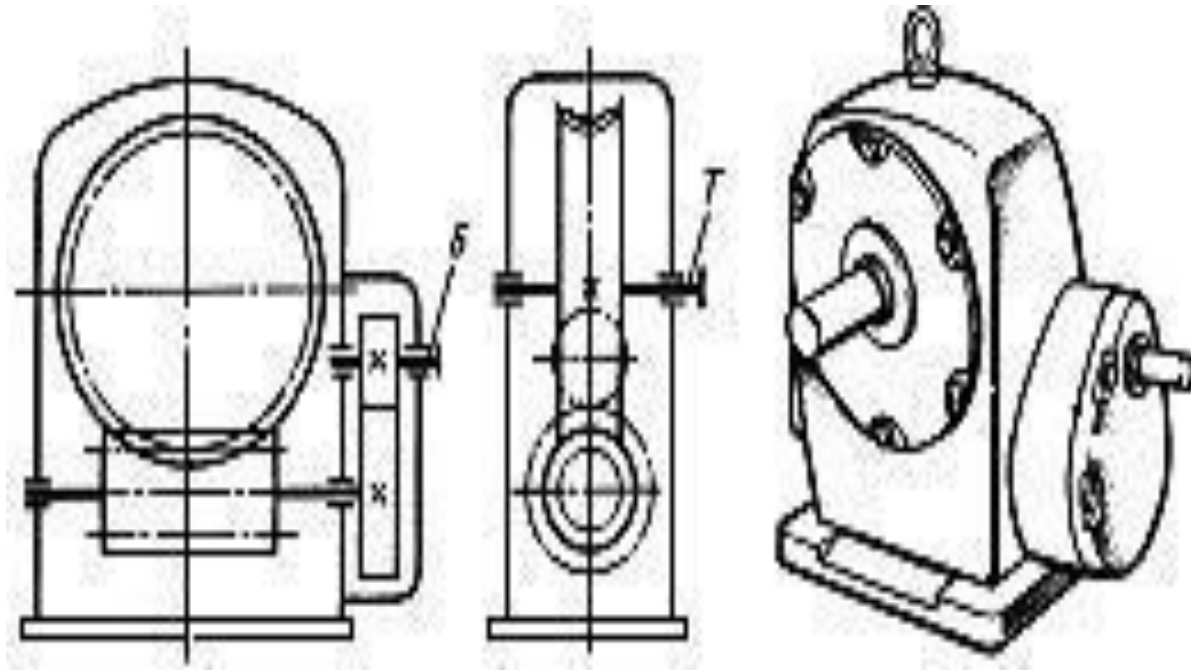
Червячно-цилиндрический двухступенчатый редуктор
